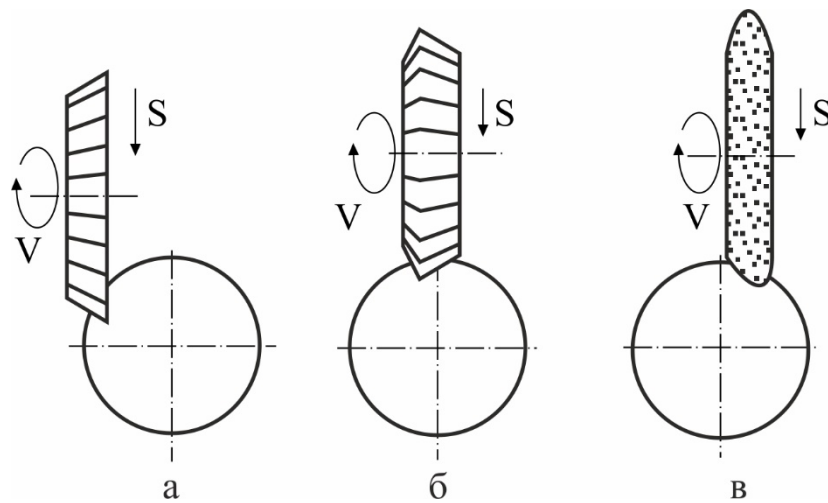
Обробка зубів відрізних пил способами копіювання однокутовими фрезами (а), двокутівими фрезами (б), шліфувальними кругами (в)
